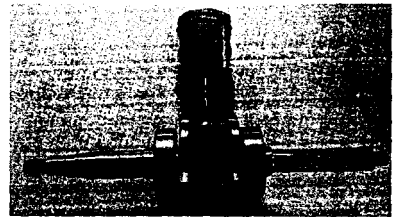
Cigüeñal con rodamientos en los apoyos (motor de 2T de pequeña cilindrada).
